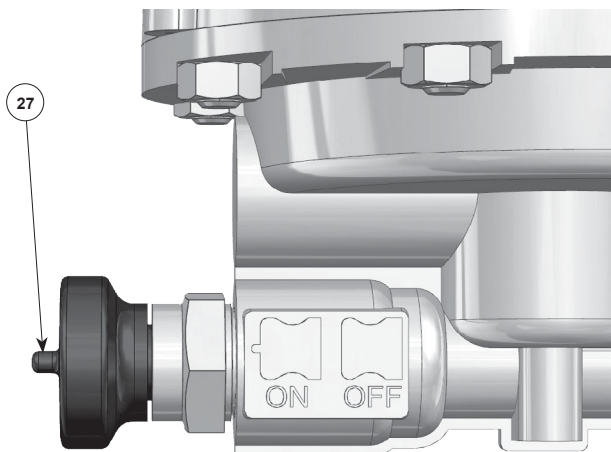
Dispositivo en Posición Abierta (Rearmada)
